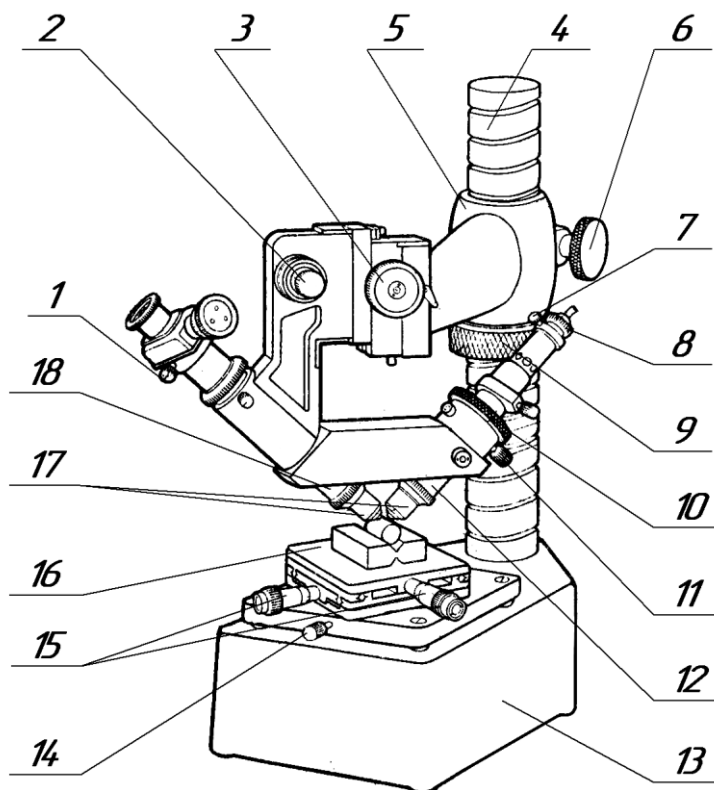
Общий вид двойного микроскопа МИС-11
